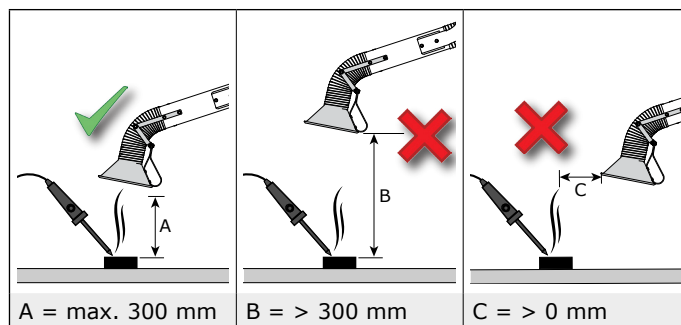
A = Position correcte de la buse (exemple : soudage)
